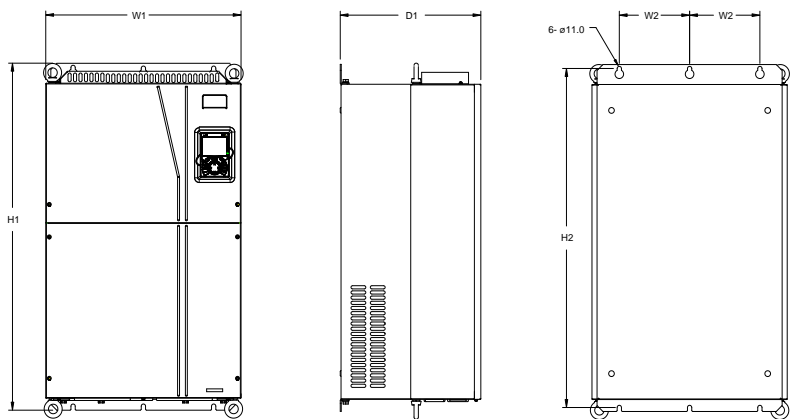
Схема настенного монтажа ПЧ 380 В, от 132 до 220 кВт
